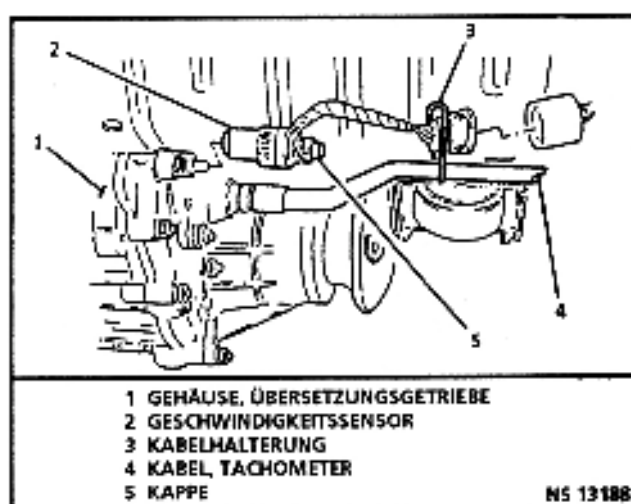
Einbaulage - Geschwindigkeitssensor
